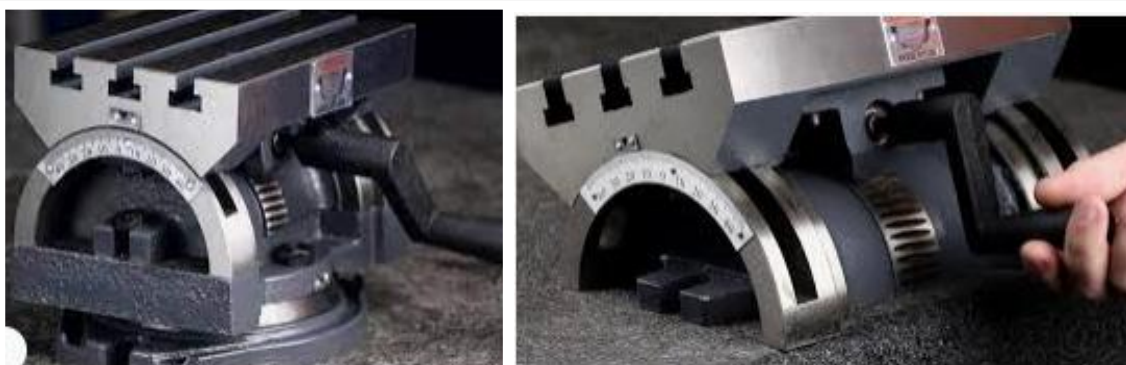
Координатный наклоняемый поворотный стол, на который будет устанавливаться разработанное приспособление для фрезерования продольного шпоночного паза на конической части вала
